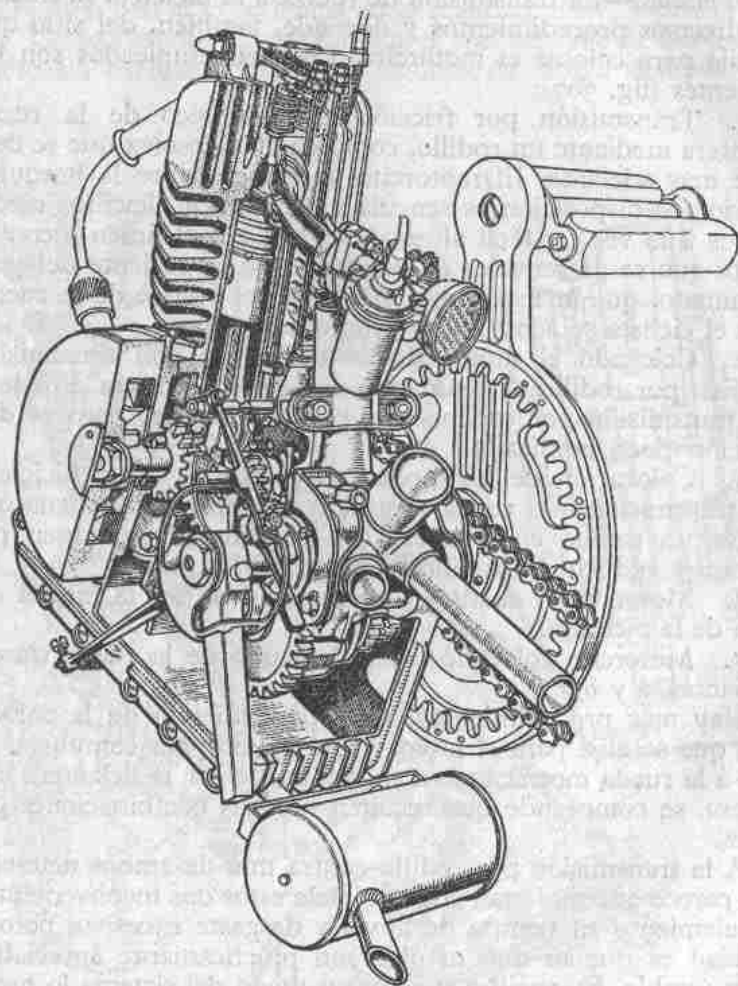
El Cucciolo (conjunto motor-transmisión, montado).
